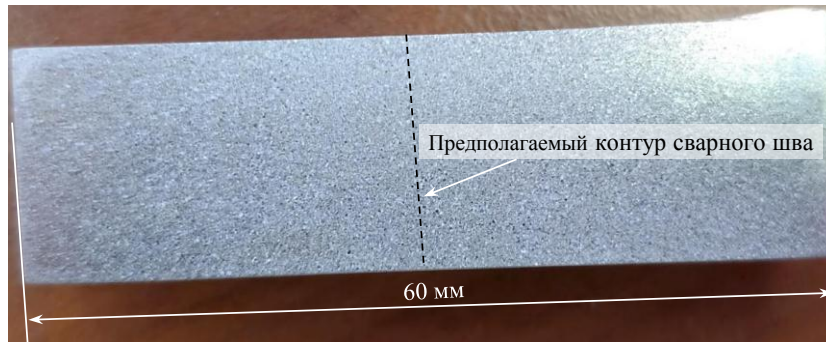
Высотный образец, изготовленный из штамповки, полученной сваркой давлением
